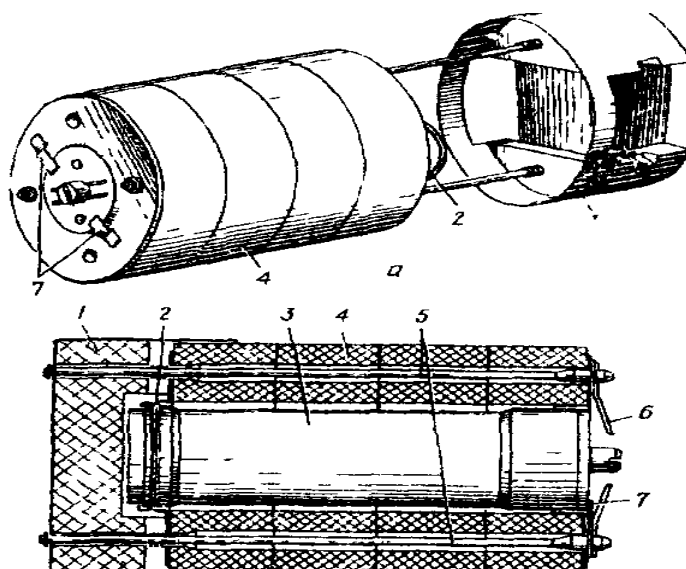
Зажигательный заряд 33-1 с поплавком:
